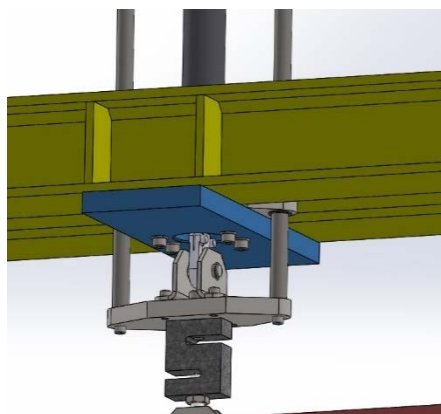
Pletina de fijación del pistón y guía del dispositivo de carga
